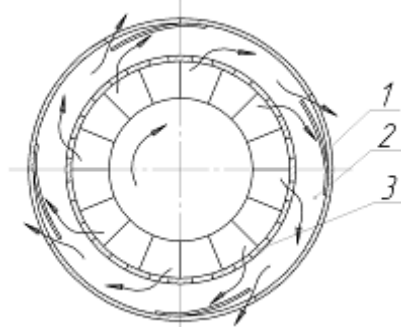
Схема перепуска воздуха из компрессора: 1 - лепестковый клапан; 2 - ресивер; 3 - направляющий аппарат с окном перепуска
